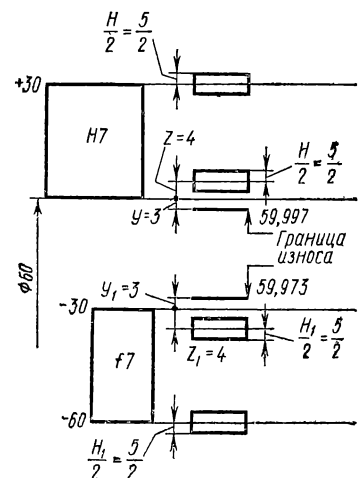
Схема расположения полей допусков на калибры по ЕСПД СЭВ
